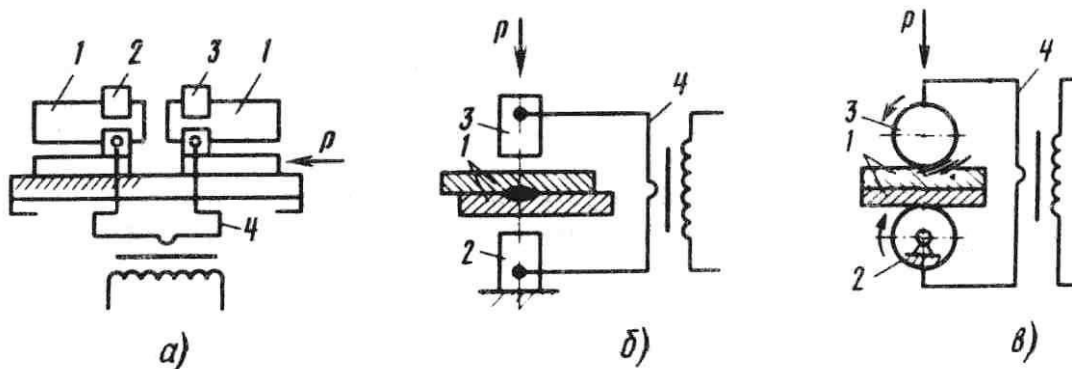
Способы контактной сварки: а — стыковая; б — точечная; в — шовная
